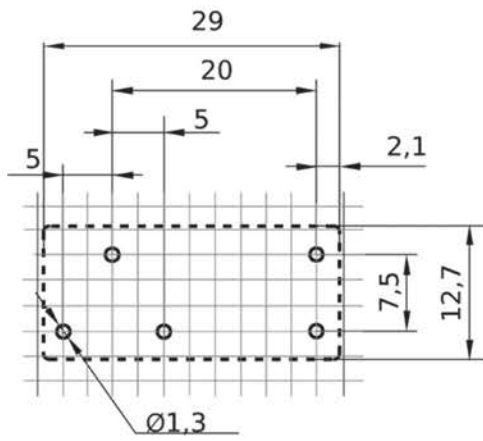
Установочные размеры для печатного монтажа для реле OptiRel G RP 41-51
